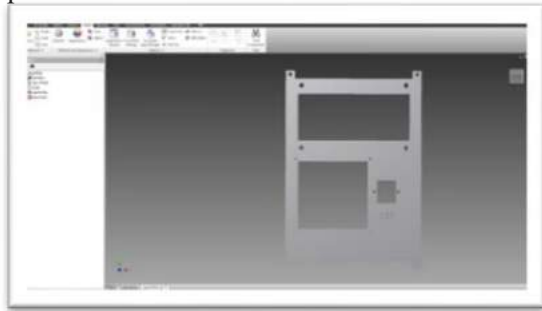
Diseño del modelo 3D del chasis del Panel de Acceso.
